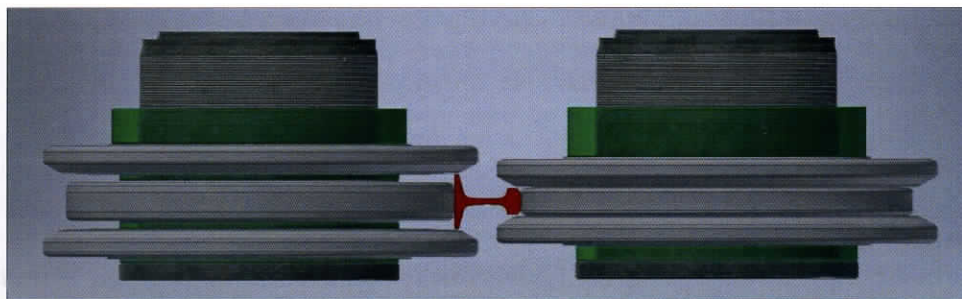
Złożenie walców klatki przedgotowej, ilustracja własna
